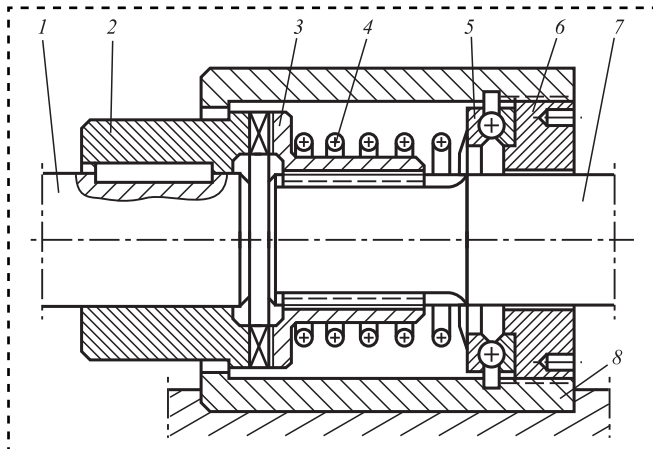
Конструкция муфты с зубчатыми полумуфтами:
